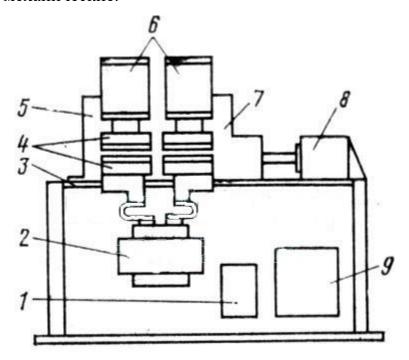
Механическое устройство установки контактно-стыковой сварки
